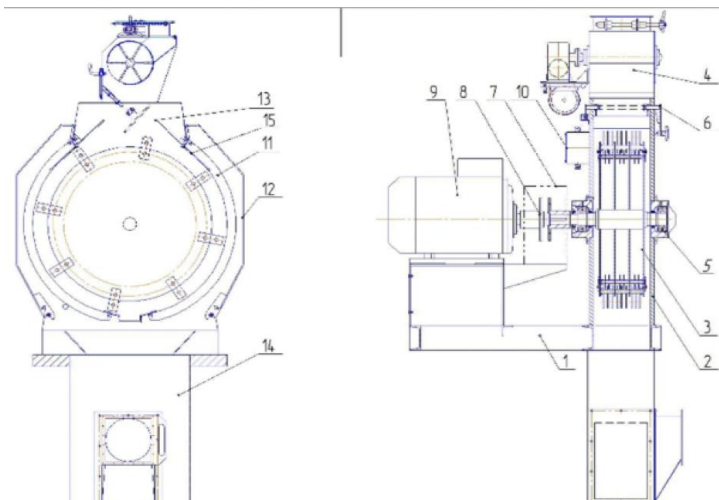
Загальний вигляд та схема молоткової дробарки марки А1-ДМ2Р: 1 - станина; 2 - корпус; 3 - ротор з молотками; 4 - живильник; 5 - корпус підшипника; 6 - клапан перекидний; 7 огорожа; 8 - муфта; 9 - електродвигун; 10 - клемний ящик; 11 - рамка з решетом; 12 - дверцята; 13 - дека; 14 - камера вибухорозрядна
